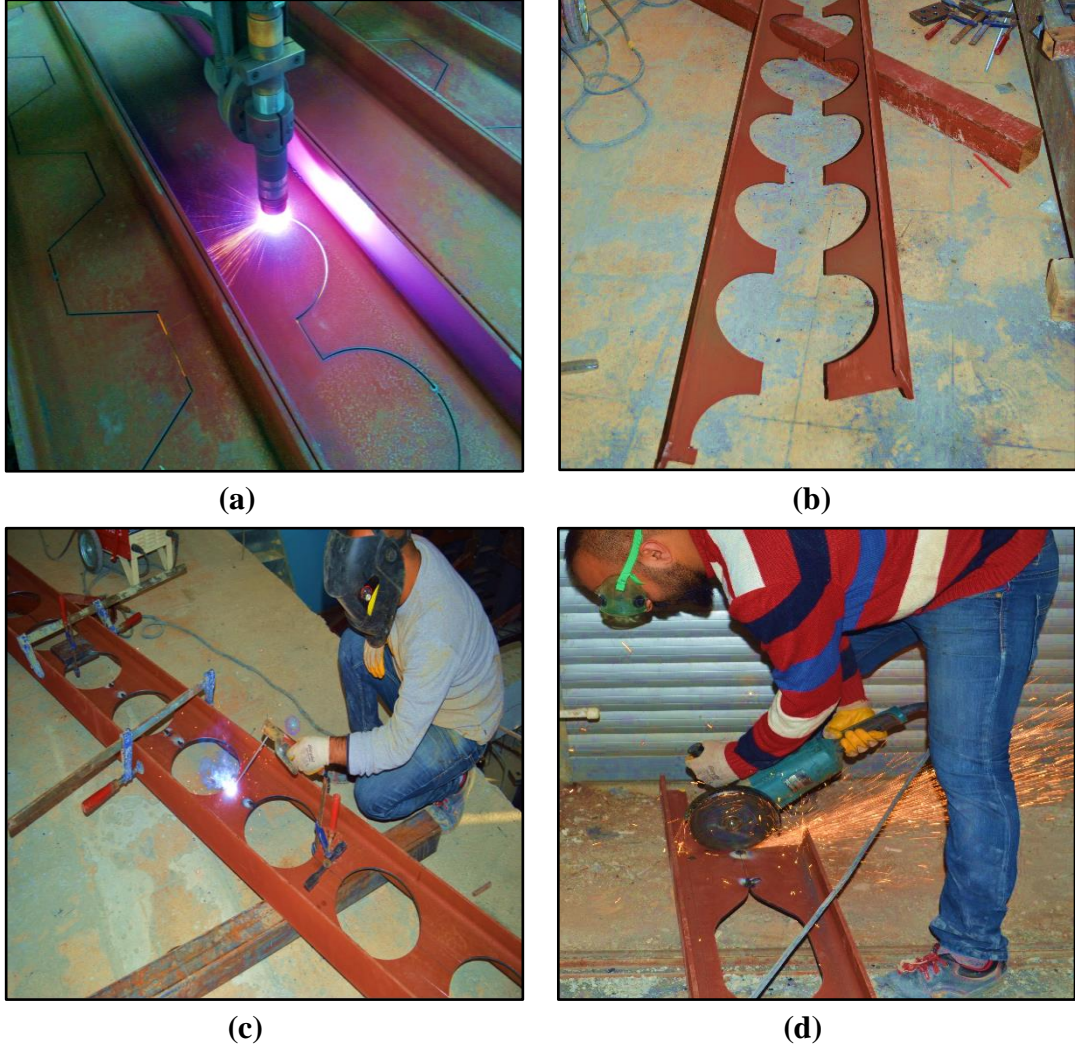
IPE 300 petek boşluklu çelik kiriş (IPE_PB_300) detayı
